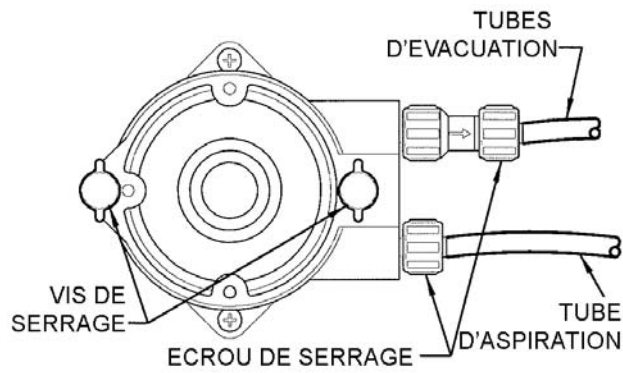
Assemblage de tête de pompe muni d'un revêtement sur l'avant de l'assemblage
